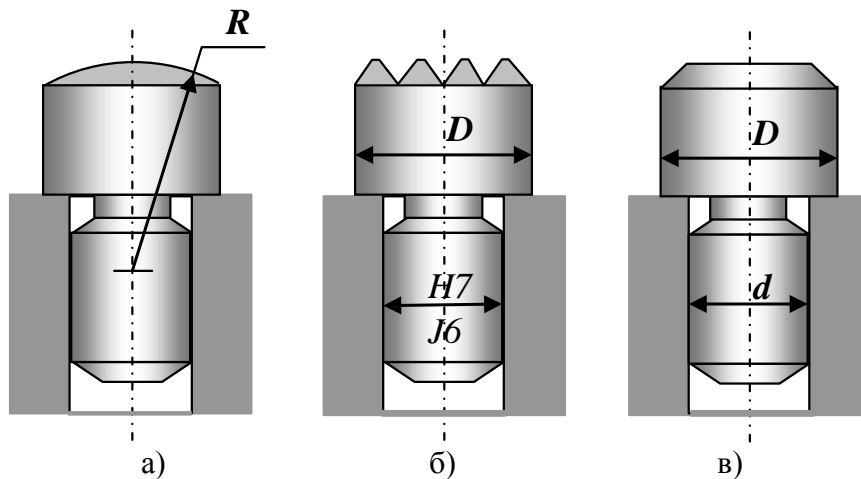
Опори для встановлення заготовок на плоскі поверхні:
